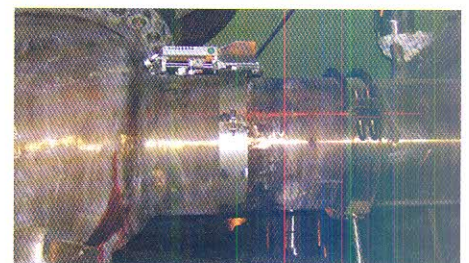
Автоматизированный голографический контроль аустенитного сварного соединения Ду500 реактора ВВЭР 440
